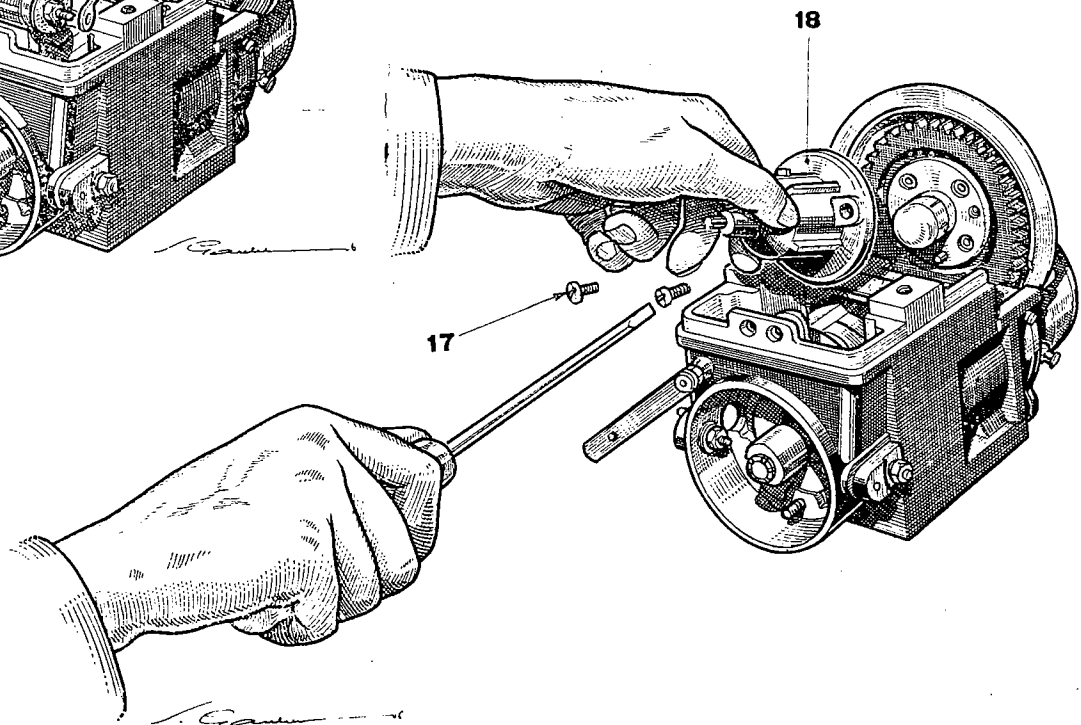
DÉMONTAGE DU CONDENSATEUR
